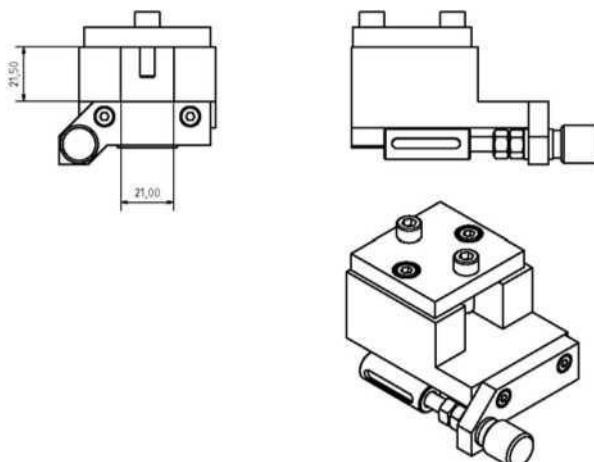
Приспособление для заточки токарного резца из высокопрочной стали
